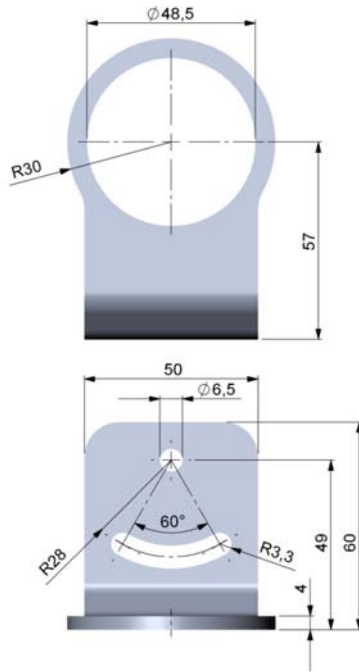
Maßzeichnung Montagewinkel, justierbar in einer Achse (TM-FB-CTL)
